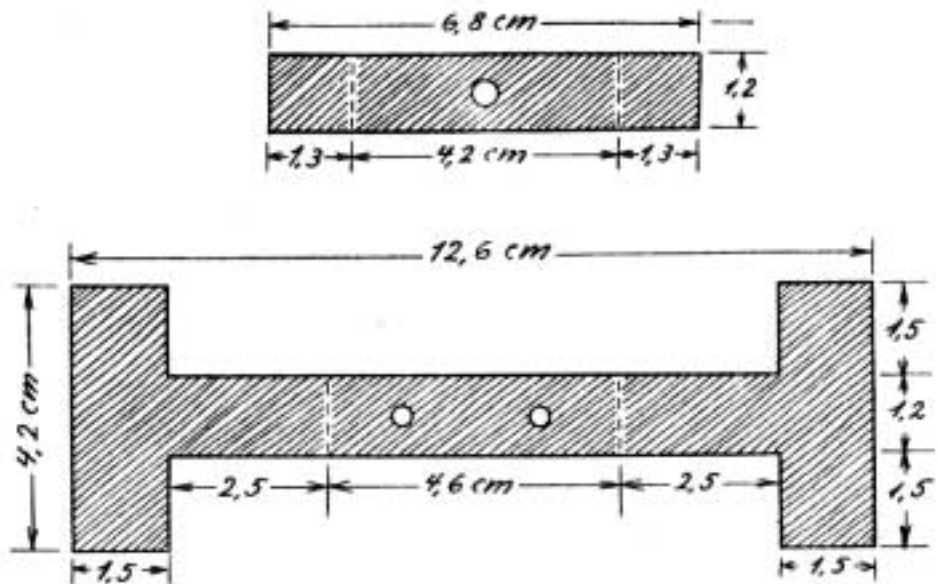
Oben: Die Blechform des Ankers. Unten: Die Blechform des Magneten. Beide Formen sind dreimal zu schneiden
